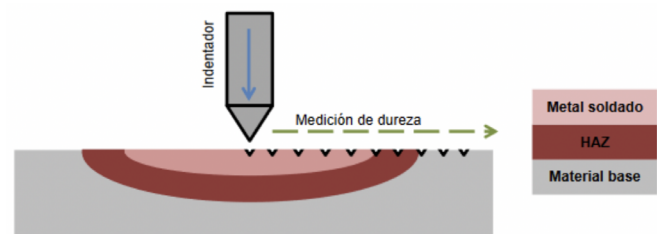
Esquema de prueba de dureza en la soldadura.
